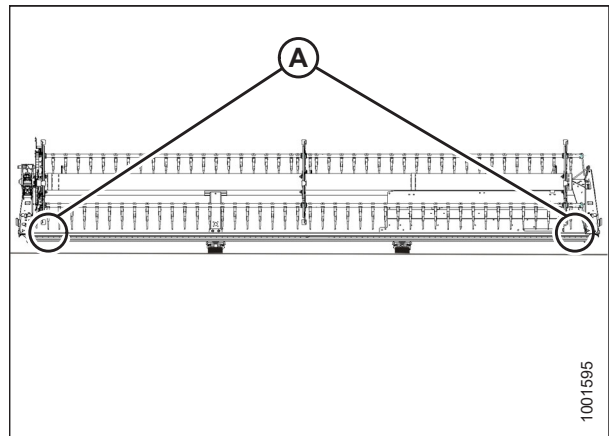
Точки вимірювання на жатці FlexDraper® — одинарне мотовило
